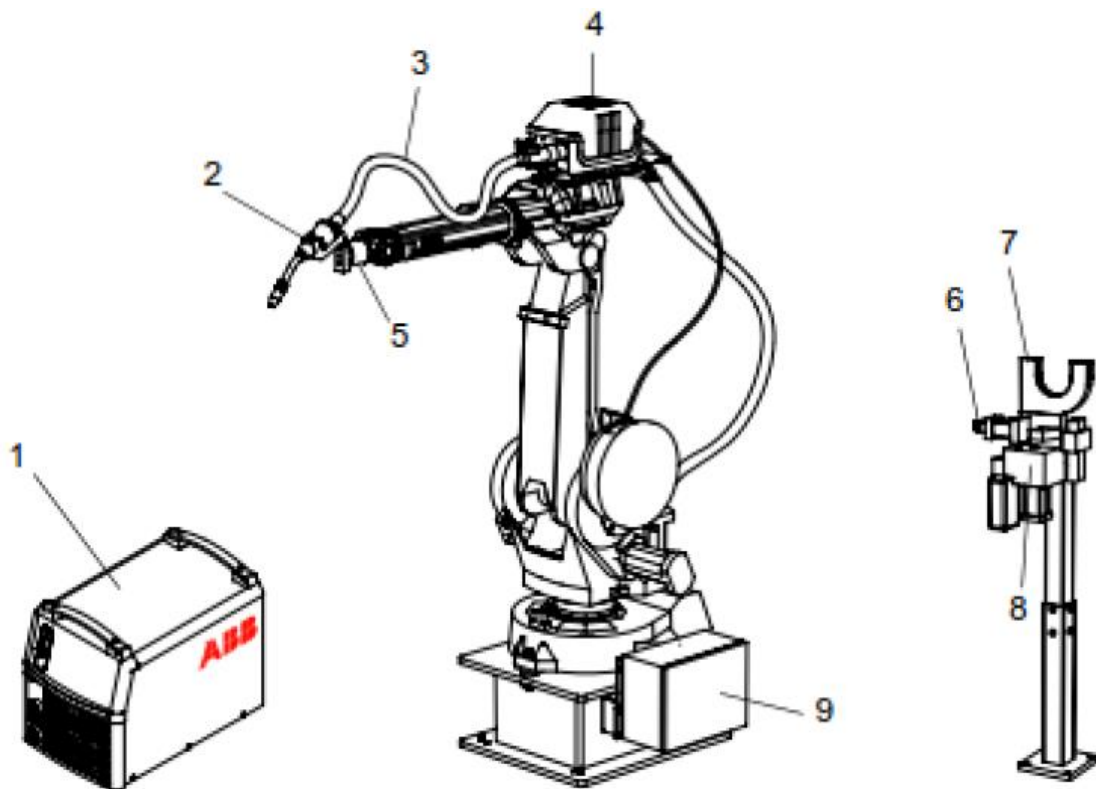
Робот IRB 2400 із встановленим зварювальним обладнанням: 1 – джерело живлення зварювальної дуги; 2 – зварювальний пальник; 3 – шлангпакет; 4 – обладнання для подачі дроту; 5 – ізолятор/датчик зіткнення (опція); 6 – різак обрізки кінця зварювального дроту; 7 – блок калібрування точки центру інструменту (ТЦІ); 8 – блок очищення сопла зварювального пальника від бризок; 9 – обладнання для управління технологічним процесом
